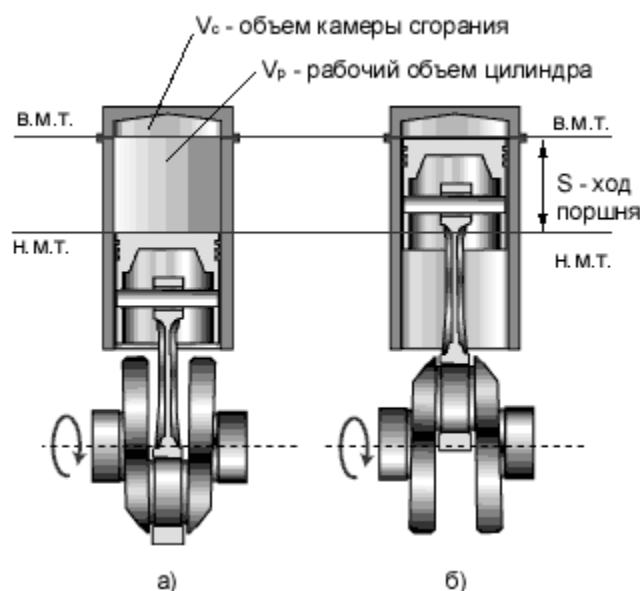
Ход поршня и объемы цилиндра двигателя
